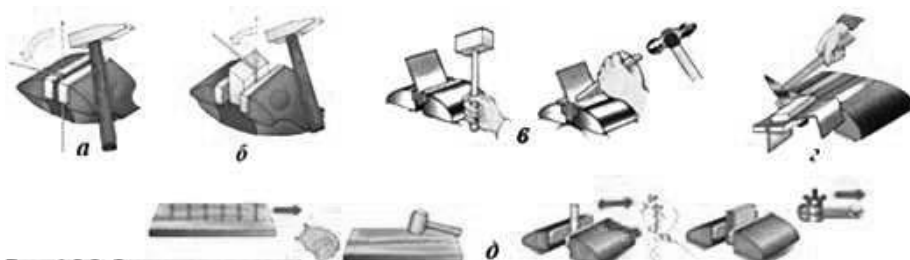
Згинання та правка деталей з листового металу та пружного дроту: а – згинання дроту на 90°; б – згинання за шаблоном кута; в, г – згинання листового металу; д – правка пружного дроту
